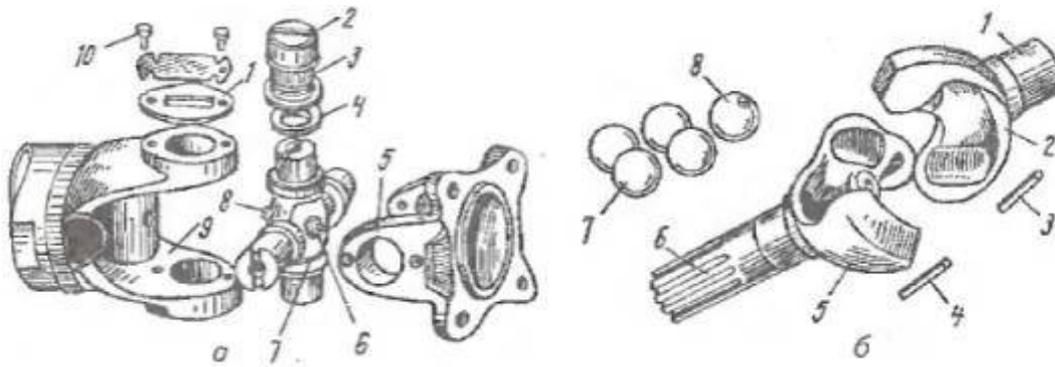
Карданные шарниры: а — карданный шарнир: 1 — крышка; 2 — стакан; 3 — игольчатый подшипник; 4 — сальник; 5, 9 — вилки; 6 — предохранительный клапан; 7 — крестовина; 8 — масленка; 10 — винт; б — карданный шарнир равных угловых скоростей: 1 — внутренняя полуось; 2 — ведущая вилка; 3, 4 — шпильки; 5 — ведомая вилка; 6 — наружная полуось; 7 — шарики; 8 — центральный шарик.
